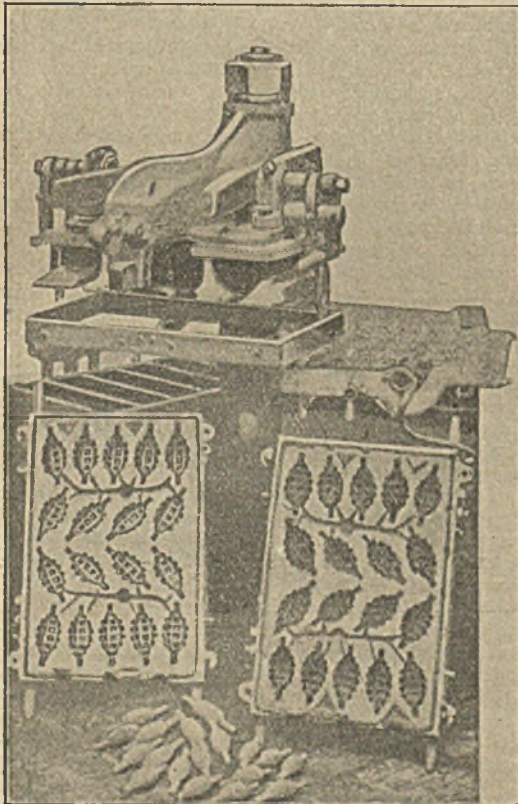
Hydraulische Formmaschine für französische Handgranaten.
